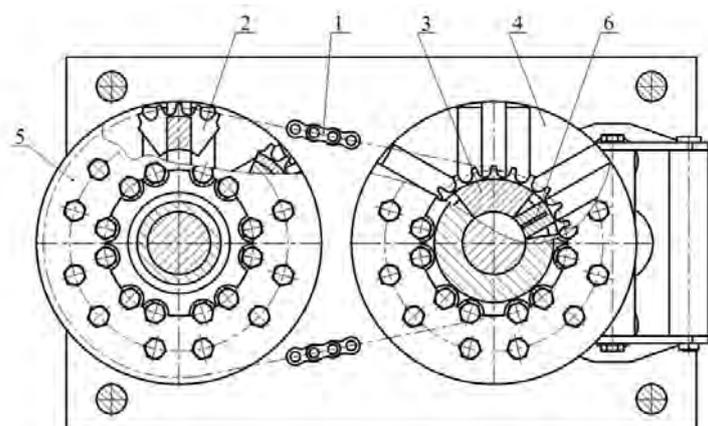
Вариатор с приводной роликовой цепью: 1 – приводная роликовая цепь; 2 – зубчатый сектор ведомой звездочки; 3 – зубчатый сектор ведущей звездочки; 4 – составная ведущая звездочка; 5 – составная ведомая звездочка; 6 – пластинчатая пружина
